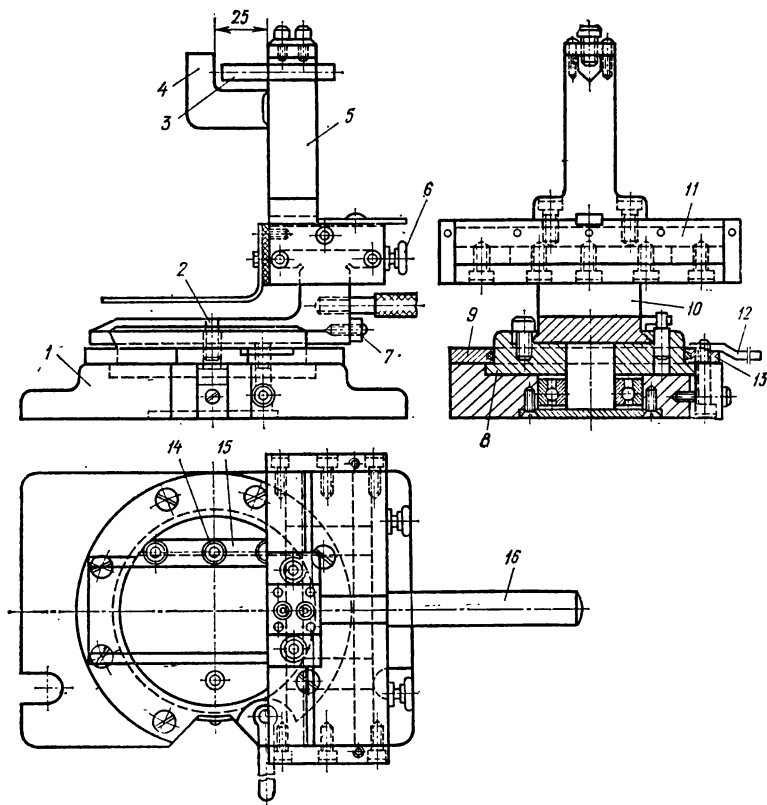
Приспособление для правки абразивных кругов со сложным профилем
